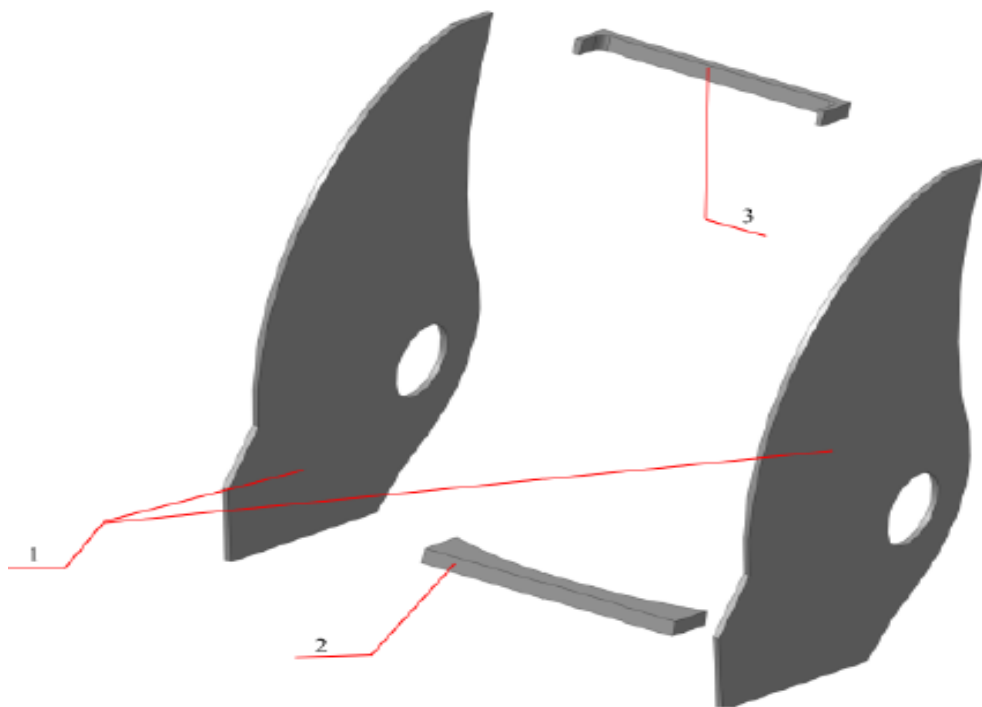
Деталювання загальне: 1 – щоки; 2 – нижня планка; 3 – верхня планка
